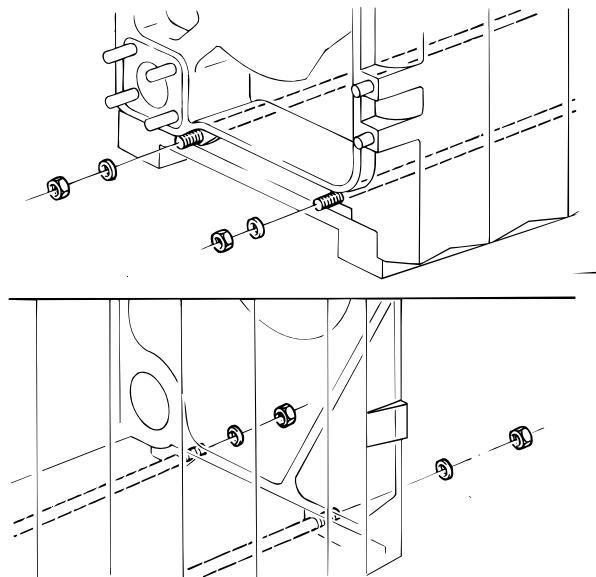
Nach dem Festschrauben der Ankerstangen Preßwerkzeug entfernen.
